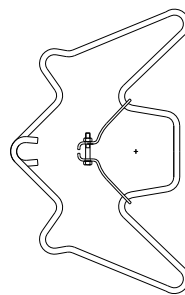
Assemblage de radiateur : Modèle U tube 60-U20
